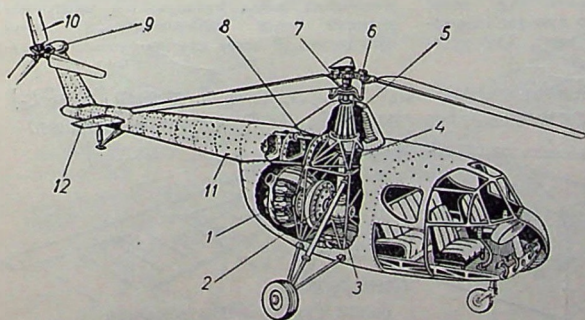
1 — мотор, 2 — вентилятор, 3 — центральный редуктор, 4 — соединительный вал, 5 — редуктор несущего винта, 6 — втулка несущего винта, 7 — автомат перекоса, 8 — вал трансмиссии рулевого винта, 9 — редуктор рулевого винта, 10 — рулевой винт, 11 — хвостовая балка, 12 — стабилизатор.
